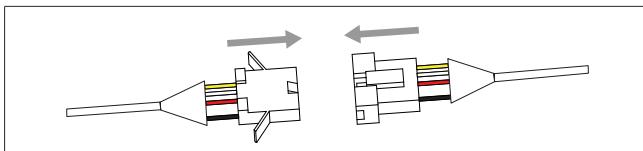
Conexión de los cables del distribuidor de aire y la unidad exterior
